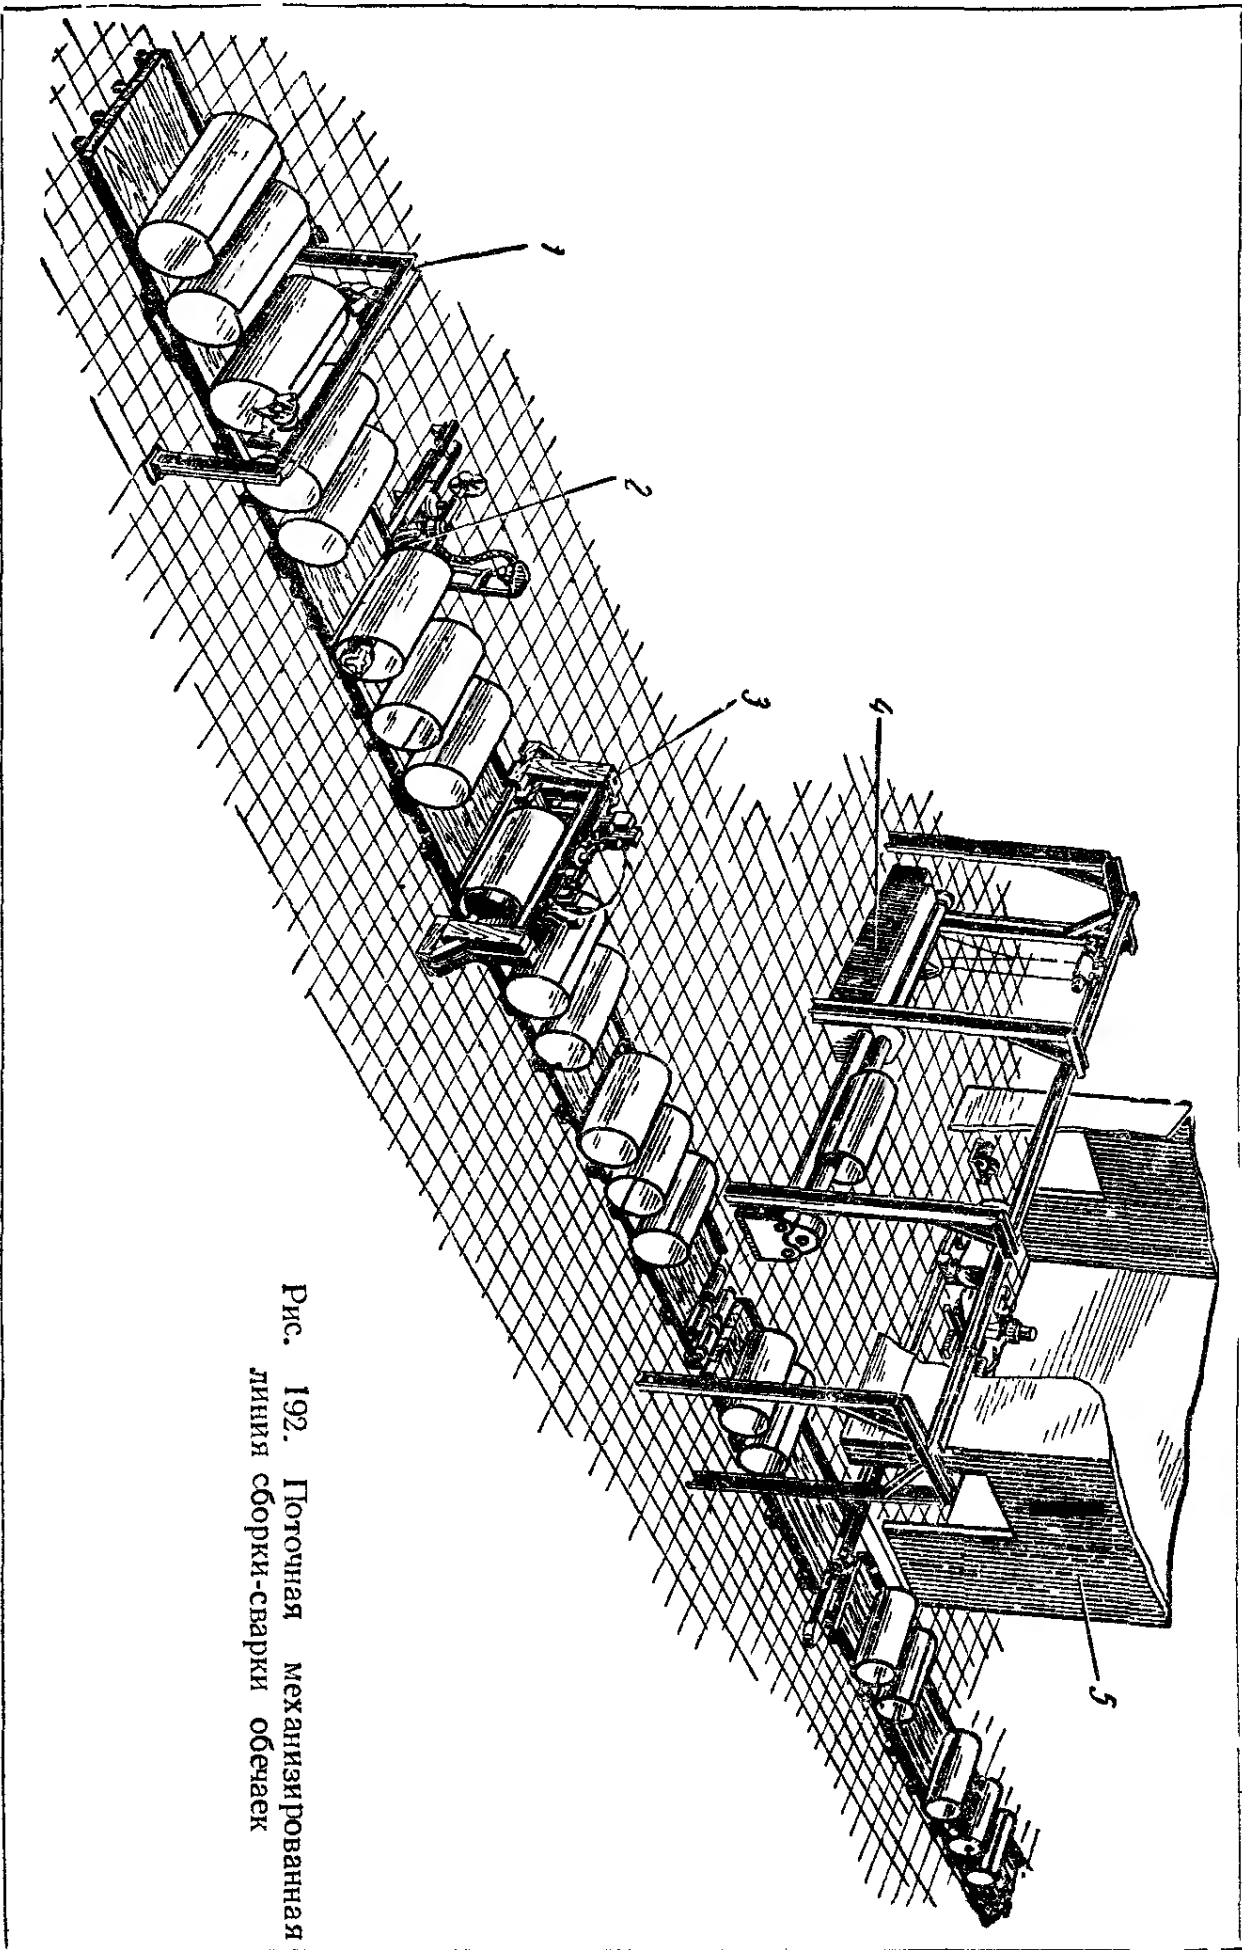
Поточная механизированная линия сборки-сварки обечаек
